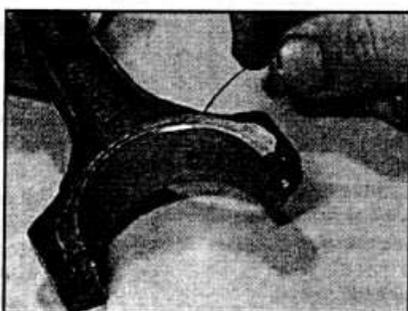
D.55. Проверка канавки для смазки в шатуне двигателя CVH.
